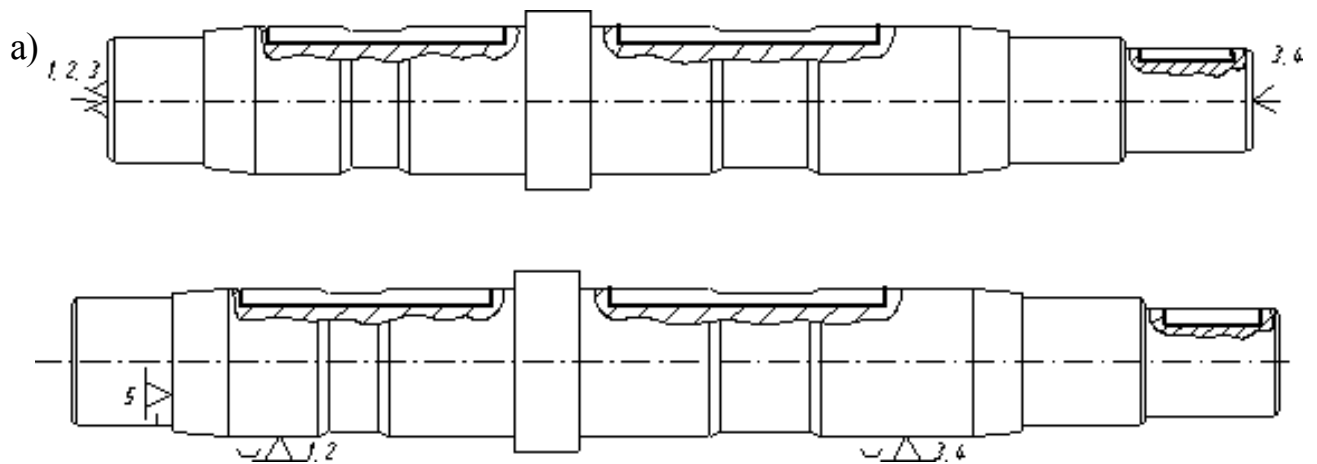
Можливі варіанти базування при фрезеруванні пазів.
